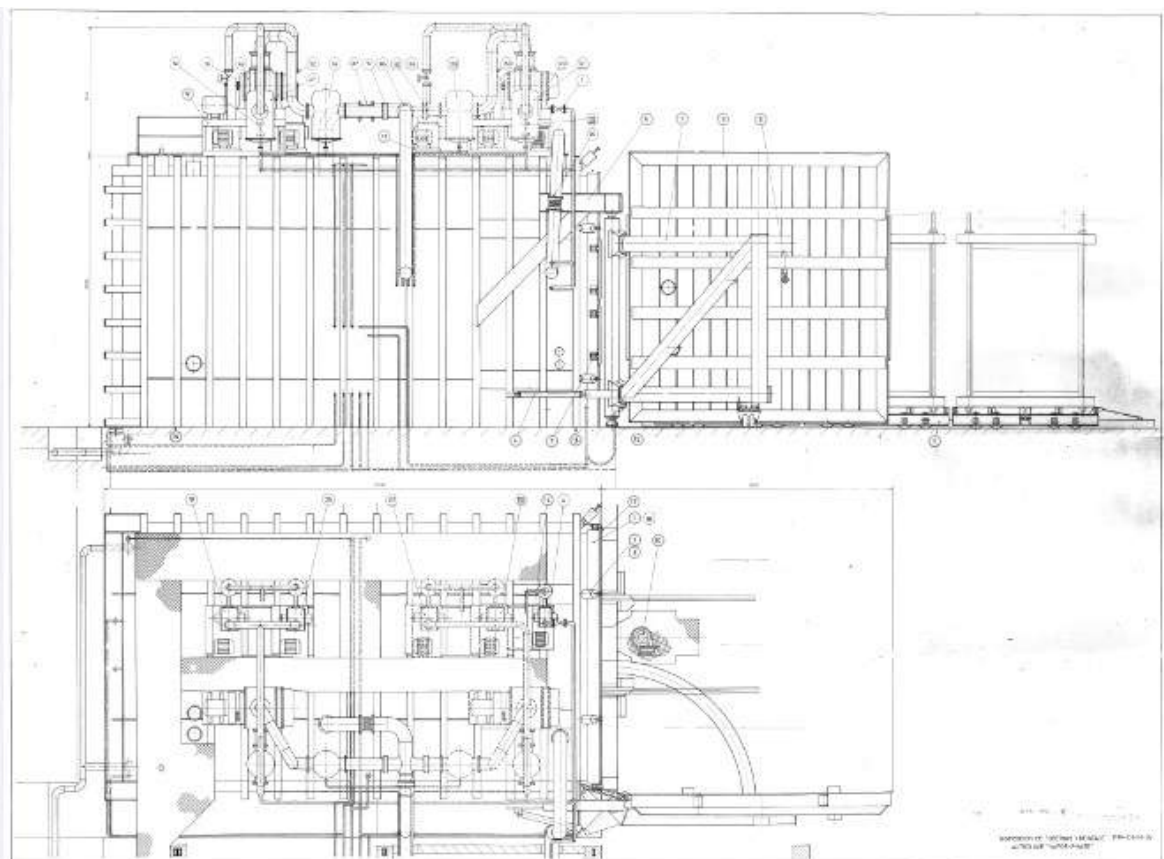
Plano de autoclave.Vista 1.
